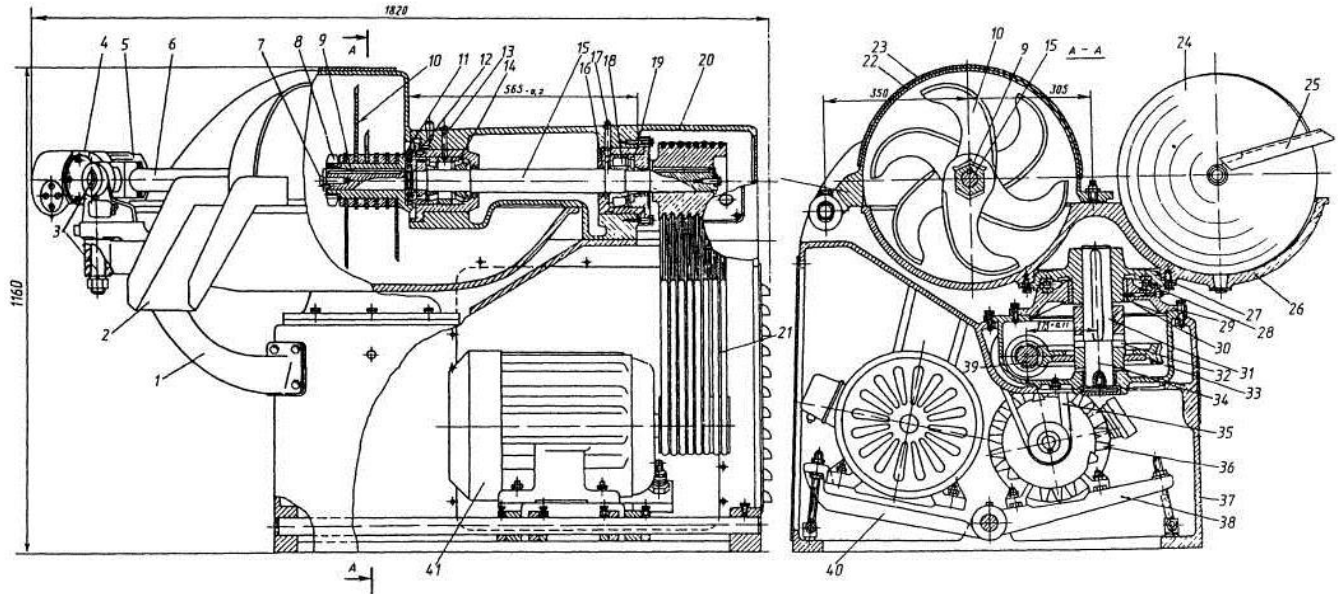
Куттер: 1 – кронштейн; 2 – лоток; 3 – вісі; 4 – черв'ячний редуктор; 5 – електродвигун вивантажувача; 6 – труба; 7 – стопорний гвинт; 8 – гайка, 9 – шпонка; 10 – ніж; 11 – втулка; 12 – лабіринтове ущільнення; 13 – масельнички; 14 – радіально-упорні конічні підшипники; 15 – ножовий вал; 16 – фланцеве ущільнення; 18 – роликів підшипник; 19 – склянка; 20 – верхня частина корпуса; 21, 35 – клиноремінні передачі; 22 – захисна кришка; 23 – сталевий лист; 24 – тарілка вивантажувача; 25 – шкребок, 26 – чаша, 27 – опора; 28 – кульковий упорний підшипник; 29 – кришка редуктора; 30 – підшипник ковзання; 31 – вал чаші; 32 – муфта; 33 – черв'ячне колесо; 34 – вісь; 36,41 – електродвигуни; 37 – основа; 38,40 – плити натяжних пристроїв; 39 – черв'як
